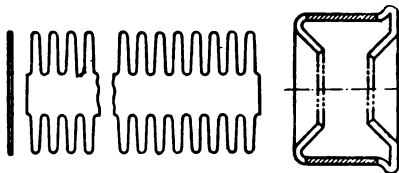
Коллектор с заготовкой пластин, штампованной из листовой меди.
